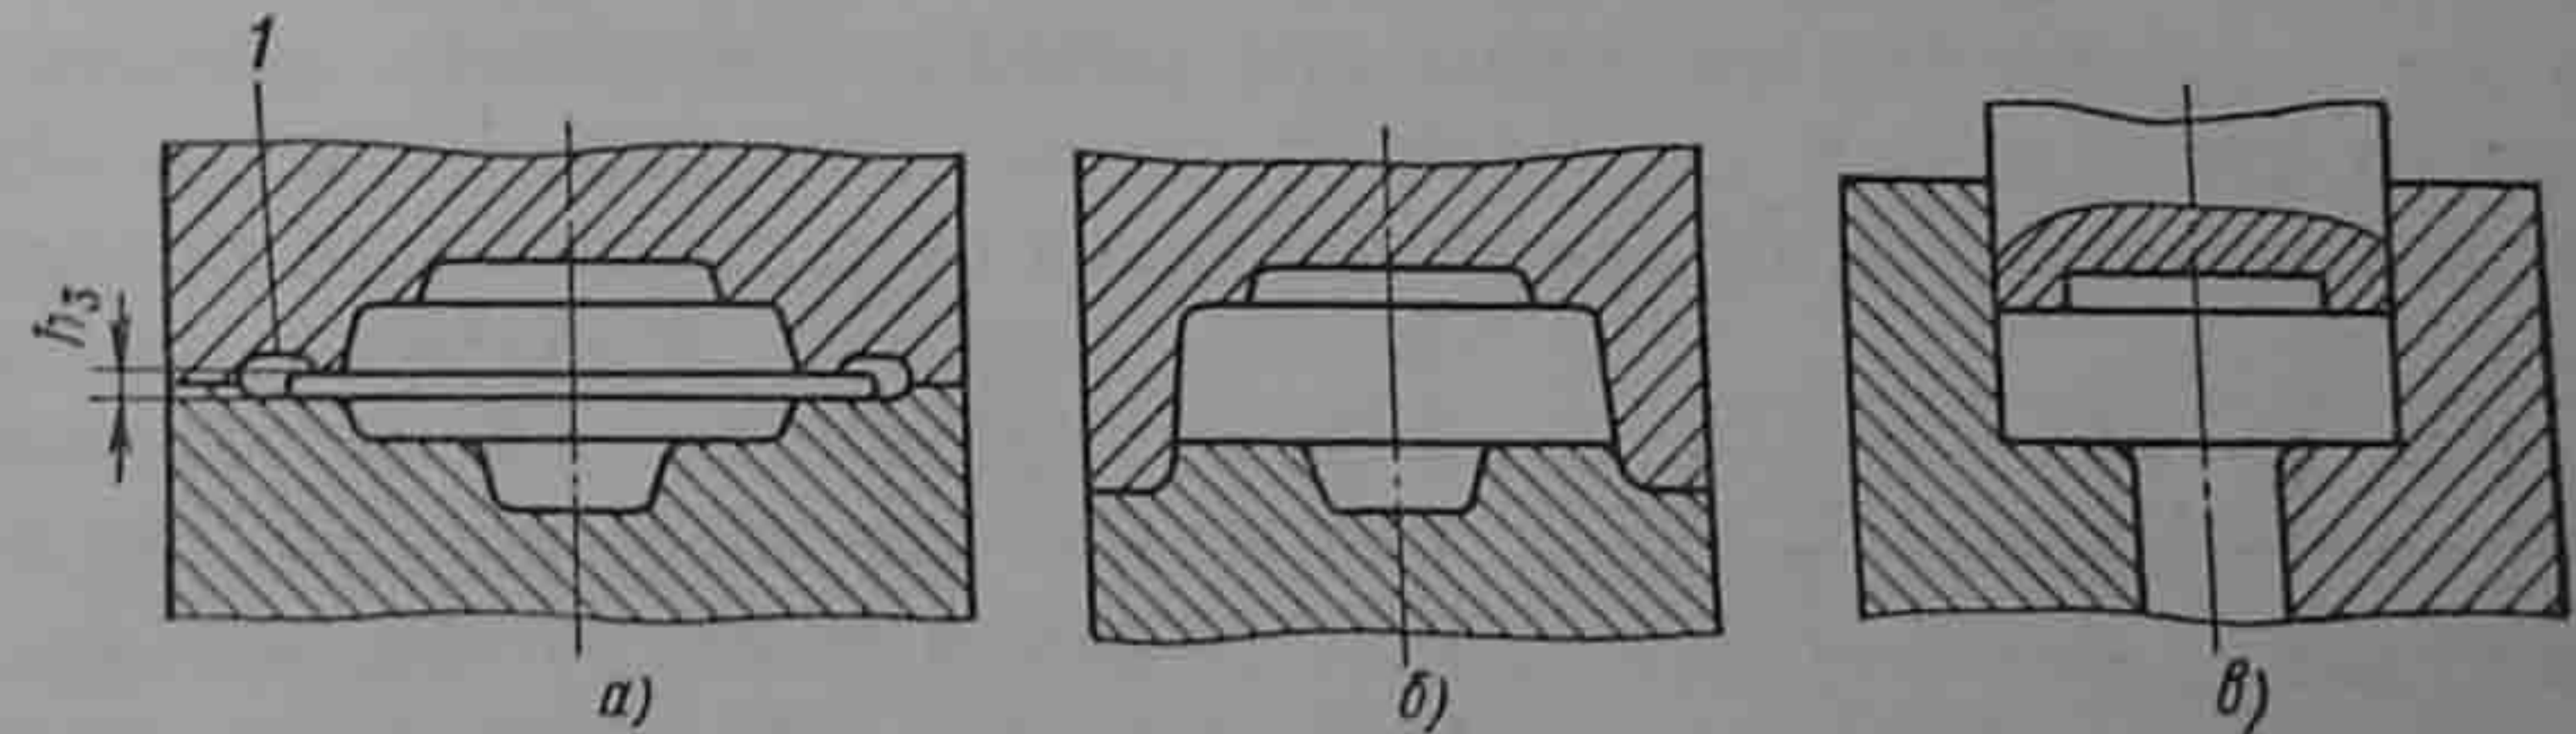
Схемы штамповки в открытых и закрытых штампах:
